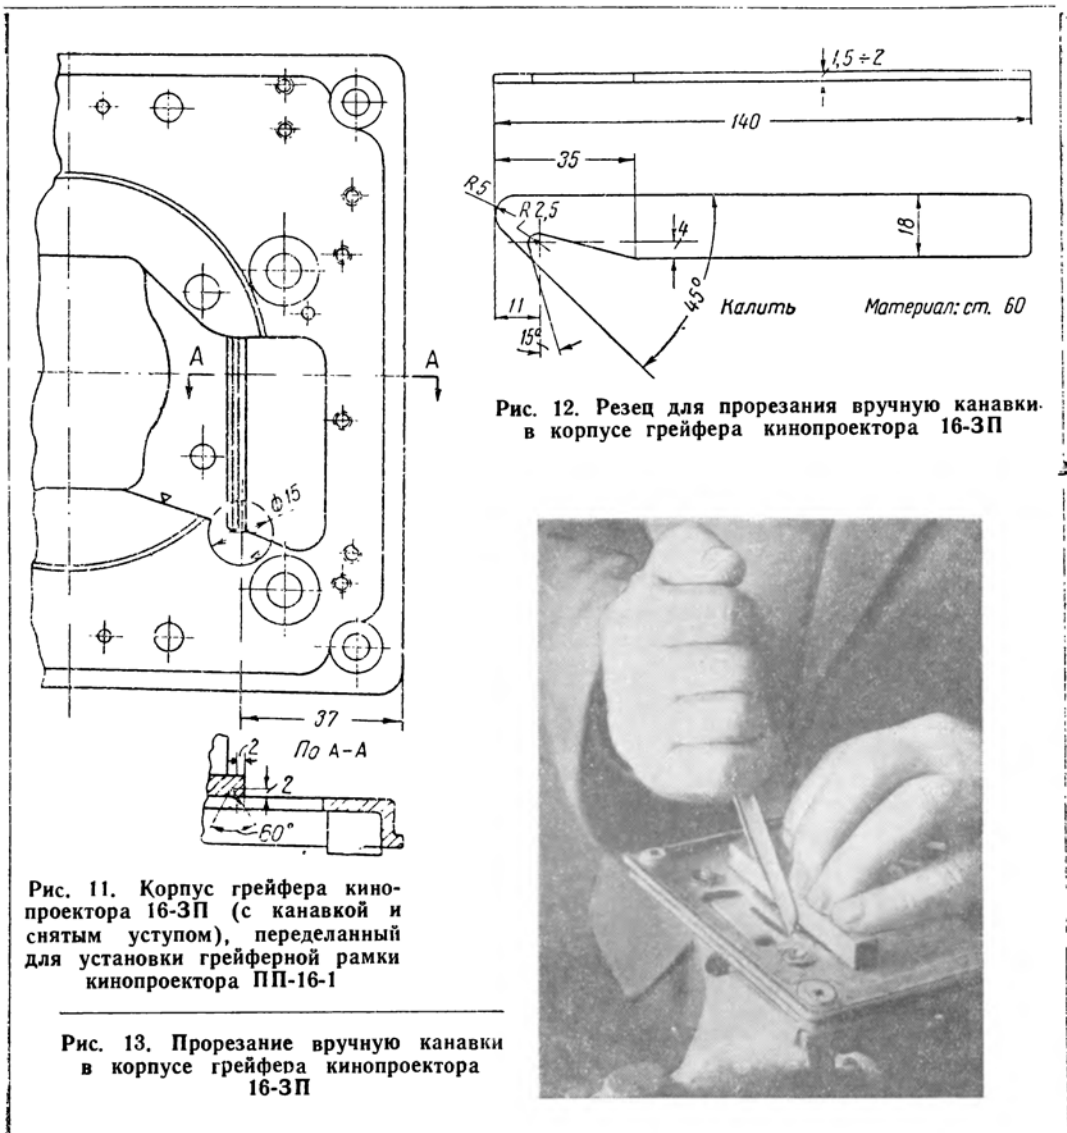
Корпус рейфера кинопроектора 16-3П (с канавкой и снятым уступом), переделанный для установки рейферной рамки кинопроектора ПП-16-1
